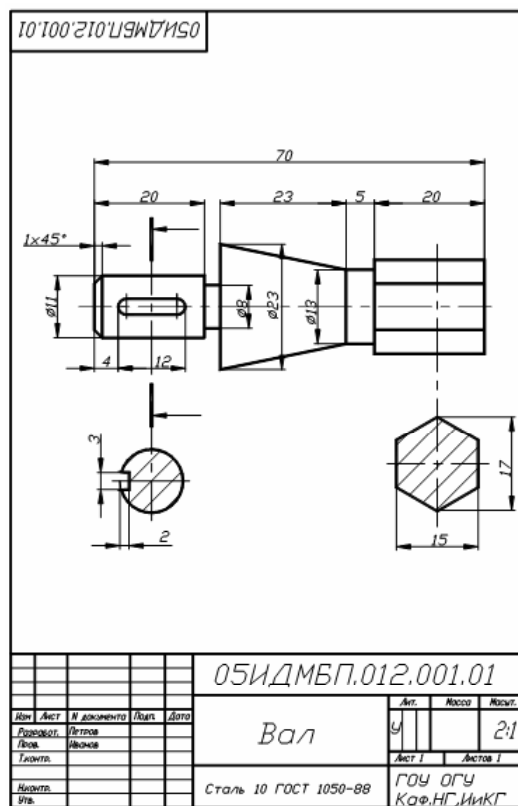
Образец выполнения чертежа детали типа «вал»
